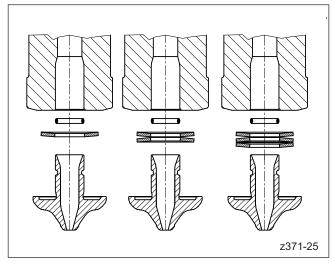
Montage der Tellerfedern, O-Ringe und Düsenspitzen
